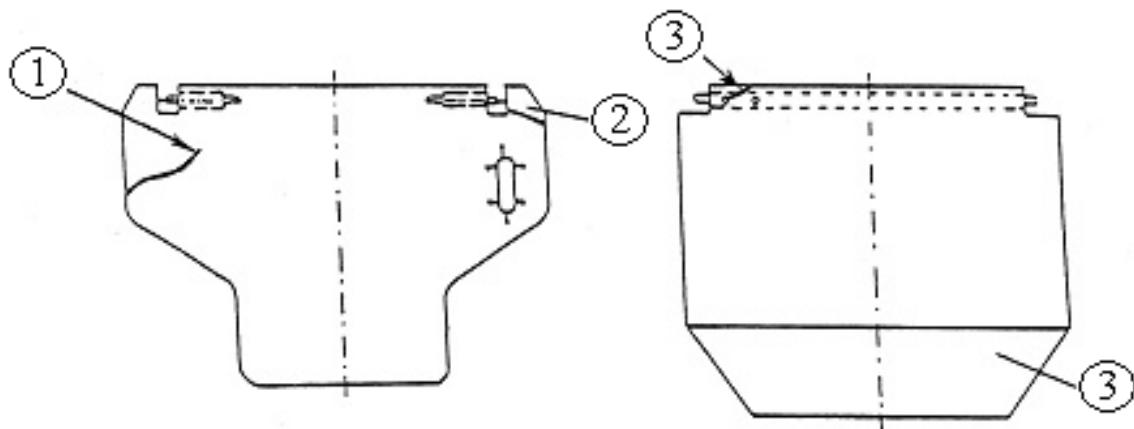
Дефекты фартука, ремонтируемые сваркой
